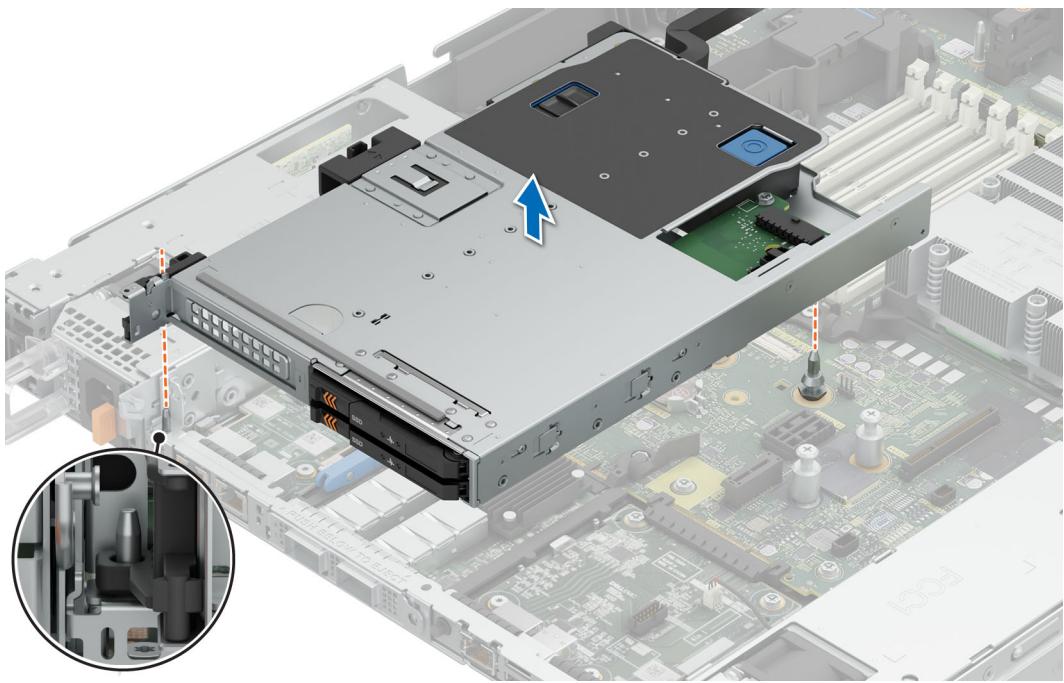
Entfernen des hinteren E3.S-Moduls
